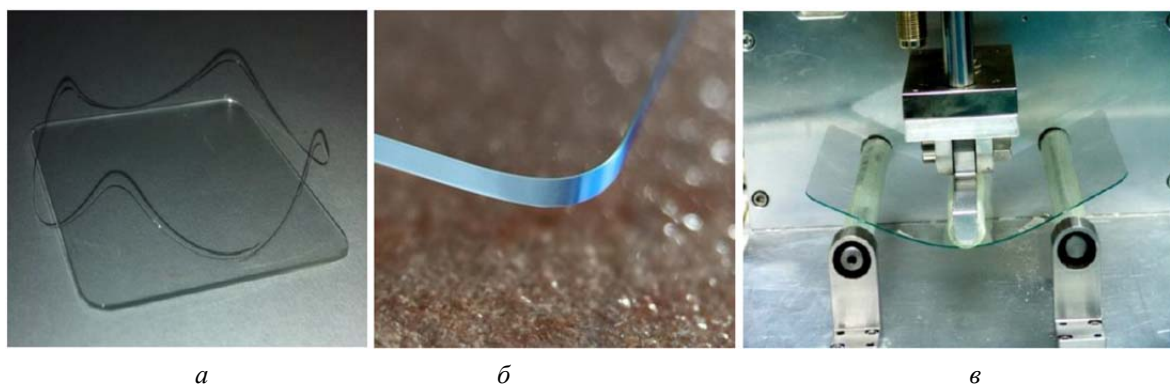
Экран iPad: а – с снятой фаской; б – кромка при увеличении $\times 60$; в – испытание на поперечный изгиб.
